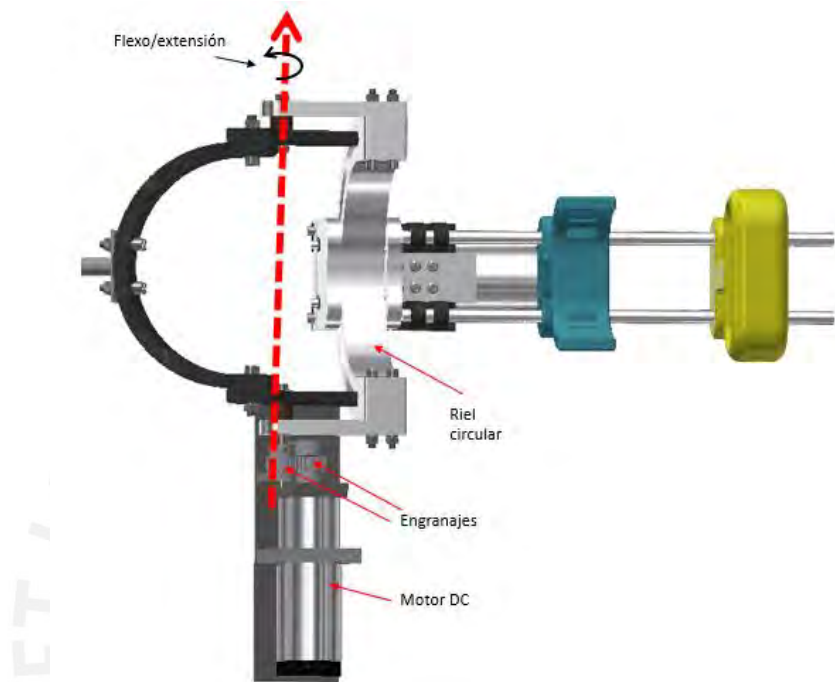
Motor DC para flexo/extensión conectado a un juego de engranajes
